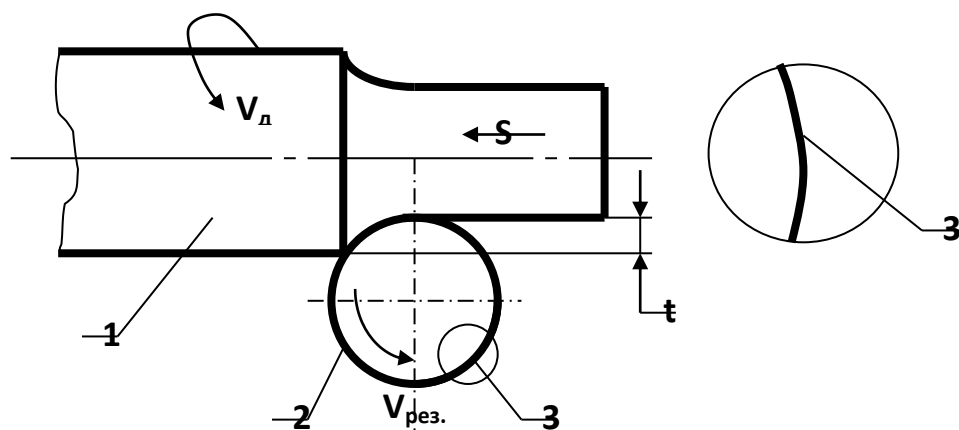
Принцип работы приспособления для точения валов с планетарной головкой. 1 – обрабатываемый материал; 2 – режущий инструмент; 3 – режущее лезвие инструмента
